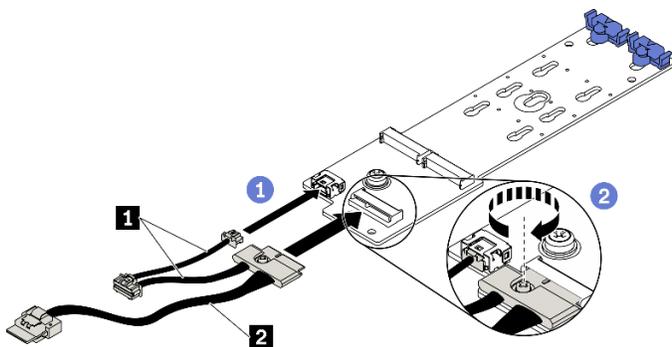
Connexion des câbles du fond de panier M.2 au fond de panier M.2
